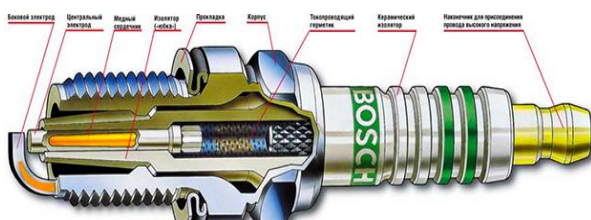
Устрій свічки запалювання з плоскою опорною поверхнею: 1 - контактна (штекерна) гайка; 2 - оребрення ізолятора (бар'єри струму); 3 – керамічний ізолятор; 4 – корпус свічки; 5 – різьбова частина корпусу; 6 – діаметр різьбової частини; 7 – керамічний ізолятор; 8 – температуростійкий ущільнювач; 9 – ущільнююче кільце; 10 - контактний стержень (центральный електрод з струмопровідним герметиком); 11 - іскровий зазор; 12 – боковий електрод ("маси").
